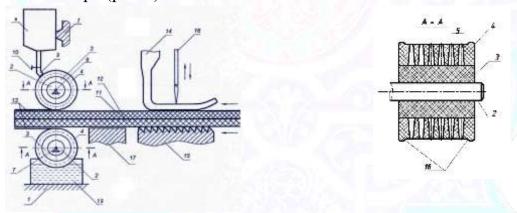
Устройства для нанесения полимерной композиции на стачиваемые детали кроя
